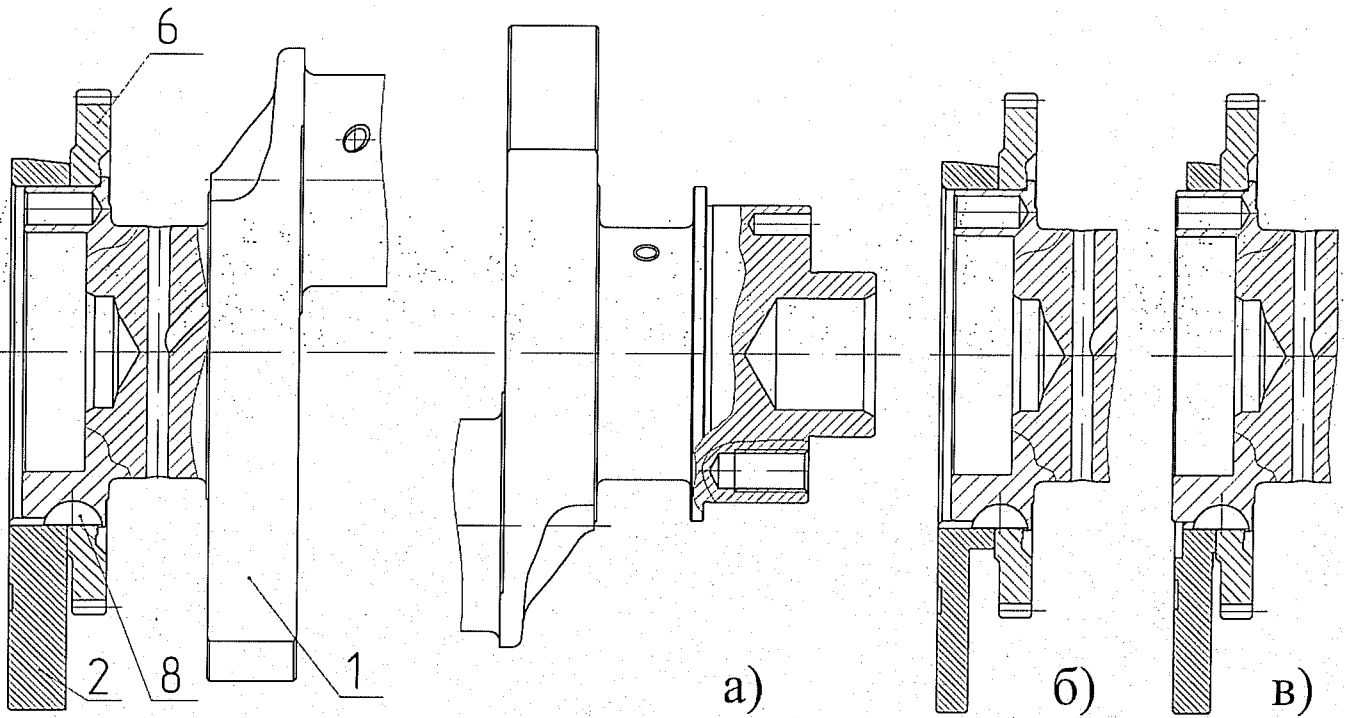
Сборочный чертеж коленчатых валов двигателей Евро-2, собранных на базе валов 740.70-1005020, 740.62-1005020 (а) и 740.30-1005020 (б, в).
